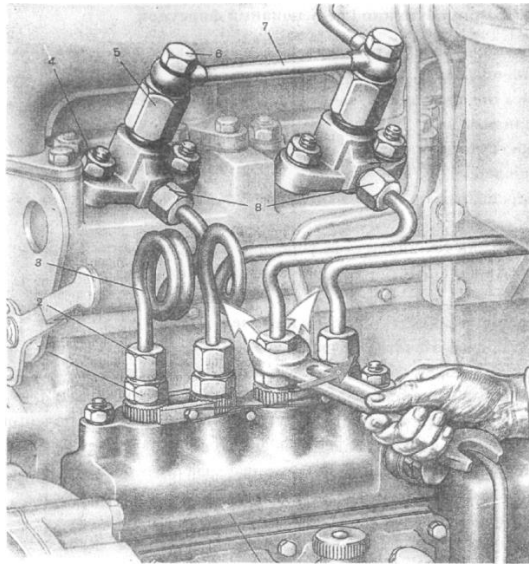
Перевірка роботи форсунок на дизелі: 1 – штуцер; 2,8 – накидні гайки; 3 – паливопровід високого тиску; 4 – гайка кріплення форсунки; 5 – ковпак форсунки; 6 – болт поворотного кутника; 7 – трубопровід низького тиску; 9 – паливний насос;
